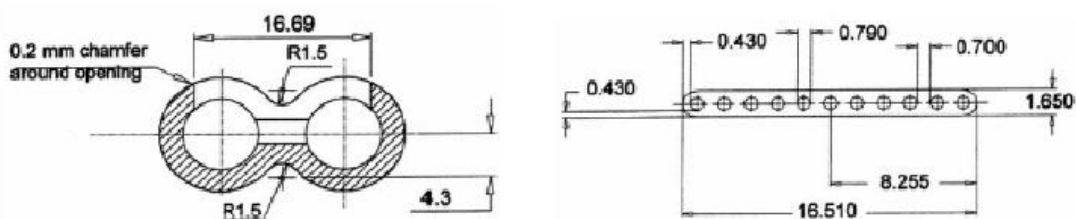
Sezione trasversale di un gas cooler con tubi piatti estrusi in alluminio.
